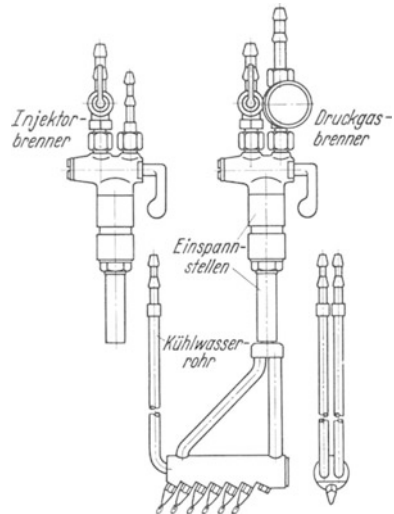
Mehrflammen-Maschinen-Schweißbrenner.
